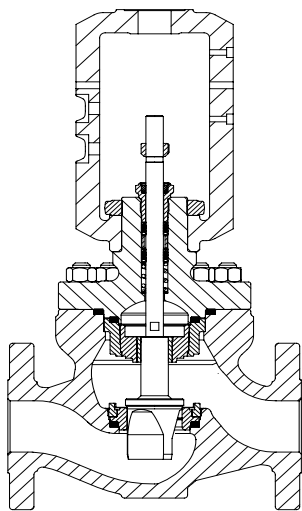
Durchgangsventil Typ 251GR mit geschraubtem Sitz
